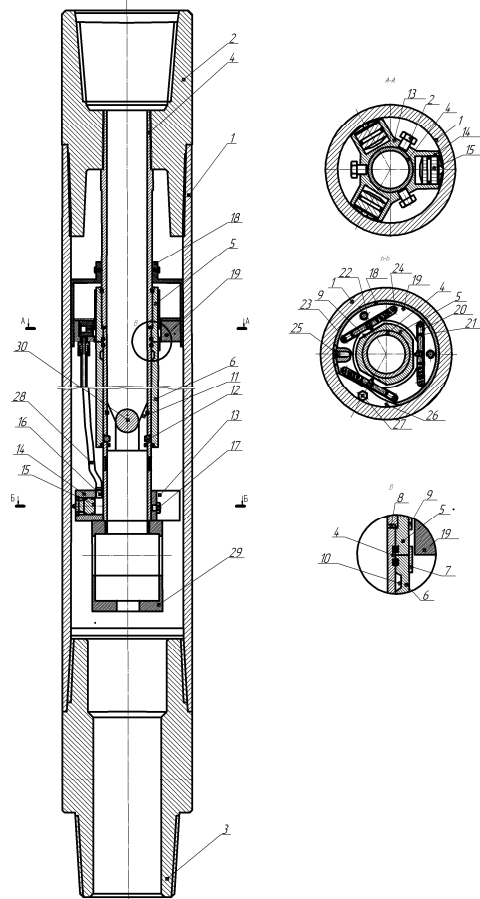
Принципова схема конструкції пристрою для вимірювання зусиль в бурильній колоні [4]
